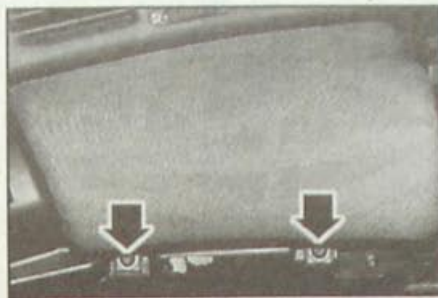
Расположение винтов крепления крышки со стороны водителя
